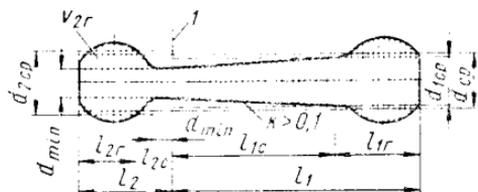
Приведение заготовки с двумя головками и стержнем к двум элементарным заготовкам:
